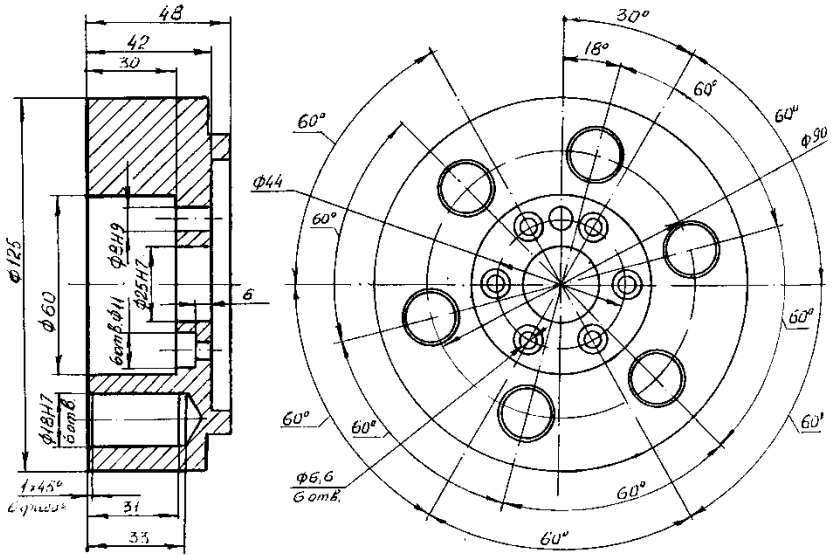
Ескізи деталей для обробки на верстаті
